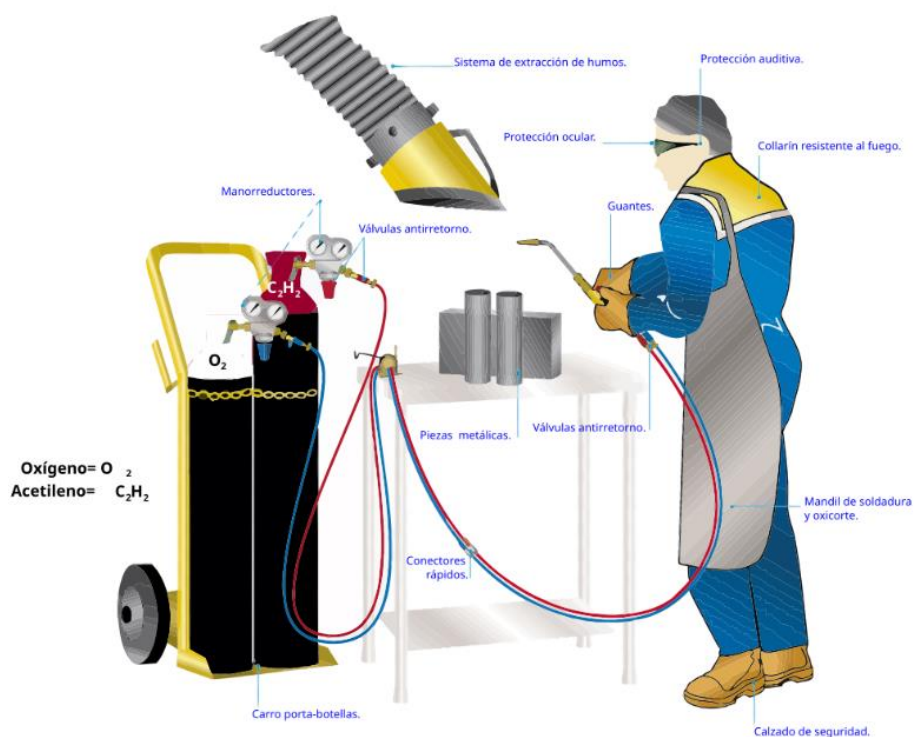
Estación de soldadura oxiacetilénica. Fuente (Wikipedia, 2025)
